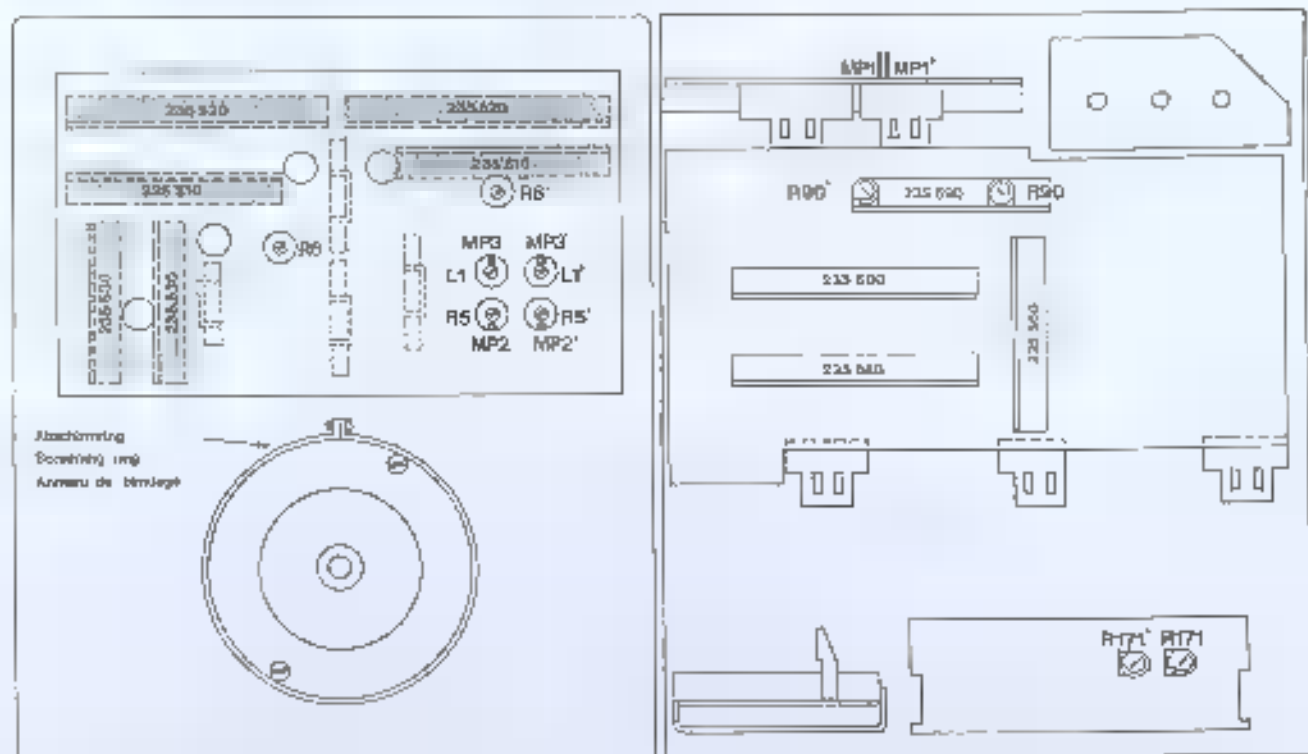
Abgleichpositionen, Geräteunterseite und Lageplan der Module
